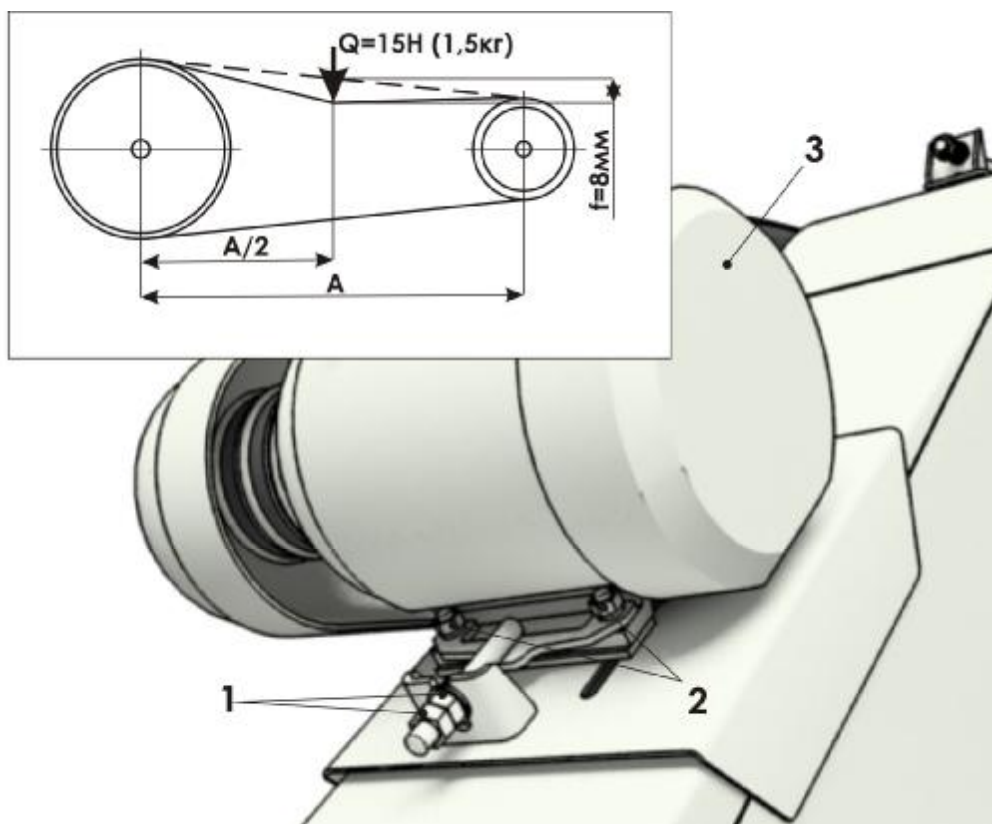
Регулировка натяжения клиноременной передачи привода загрузочного транспортера
